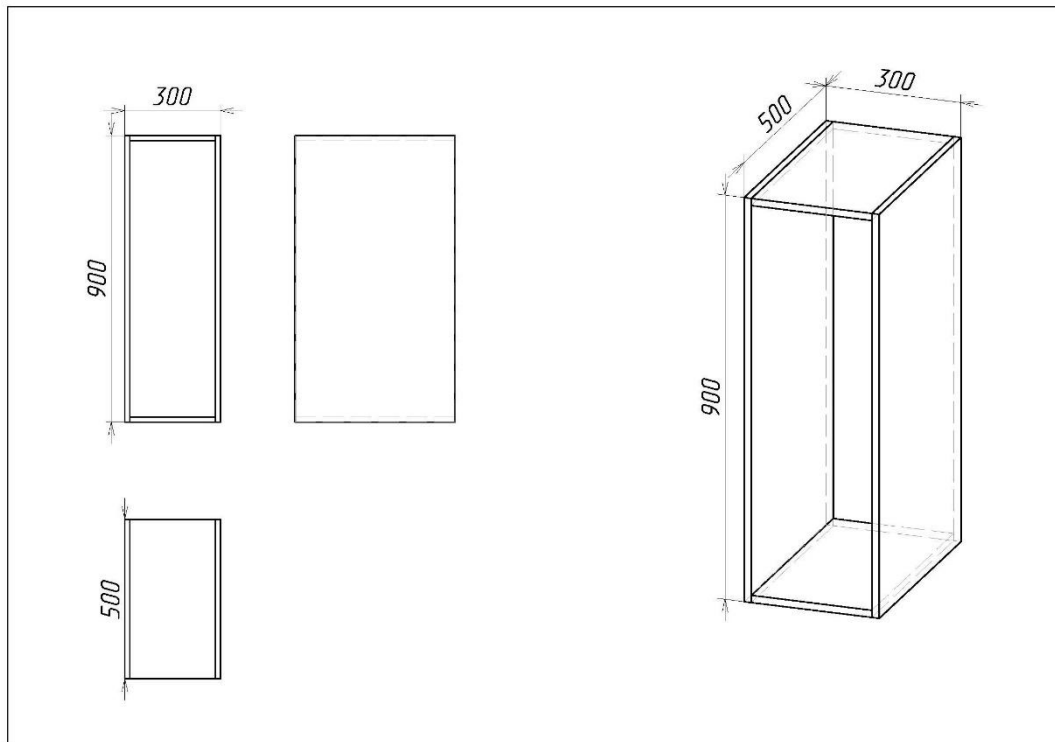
Корпус – крышка и дно вкладные (БМ)
